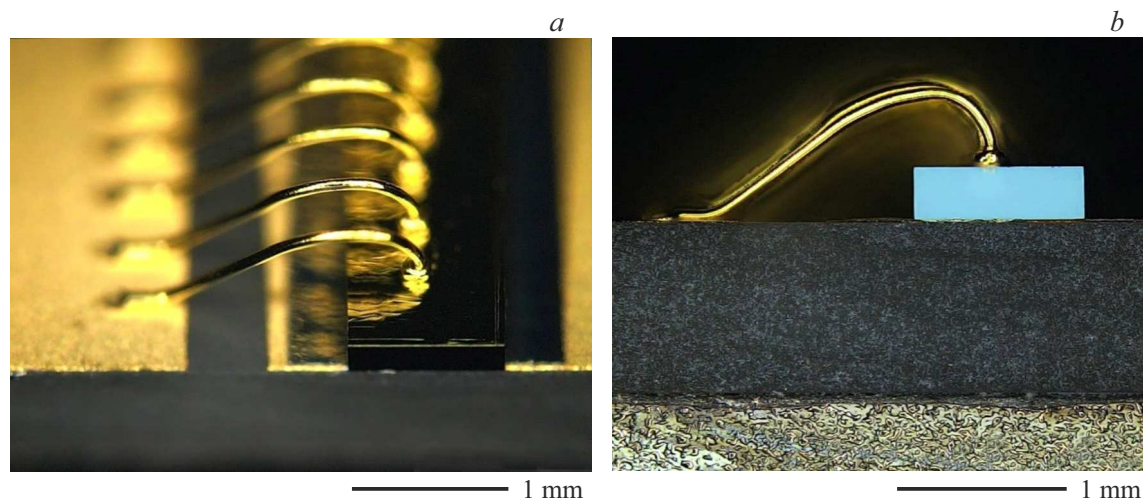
Смонтированный лазерный диод на контактной пластине: *a* — вид сверху, *b* — вид спереди.
